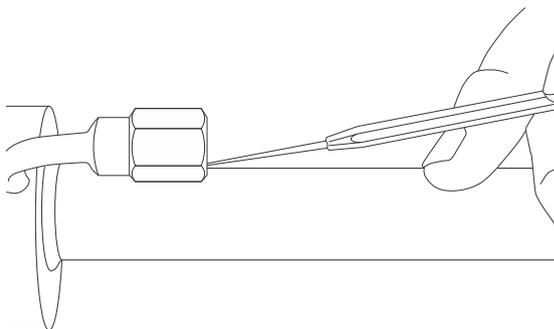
Überschüssiges Dichtungsband vom Flansch entfernen
